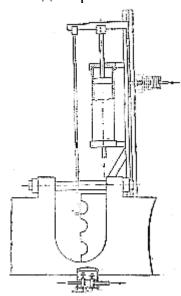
Пневматический подъемник для горизонтально-ковочной машины
